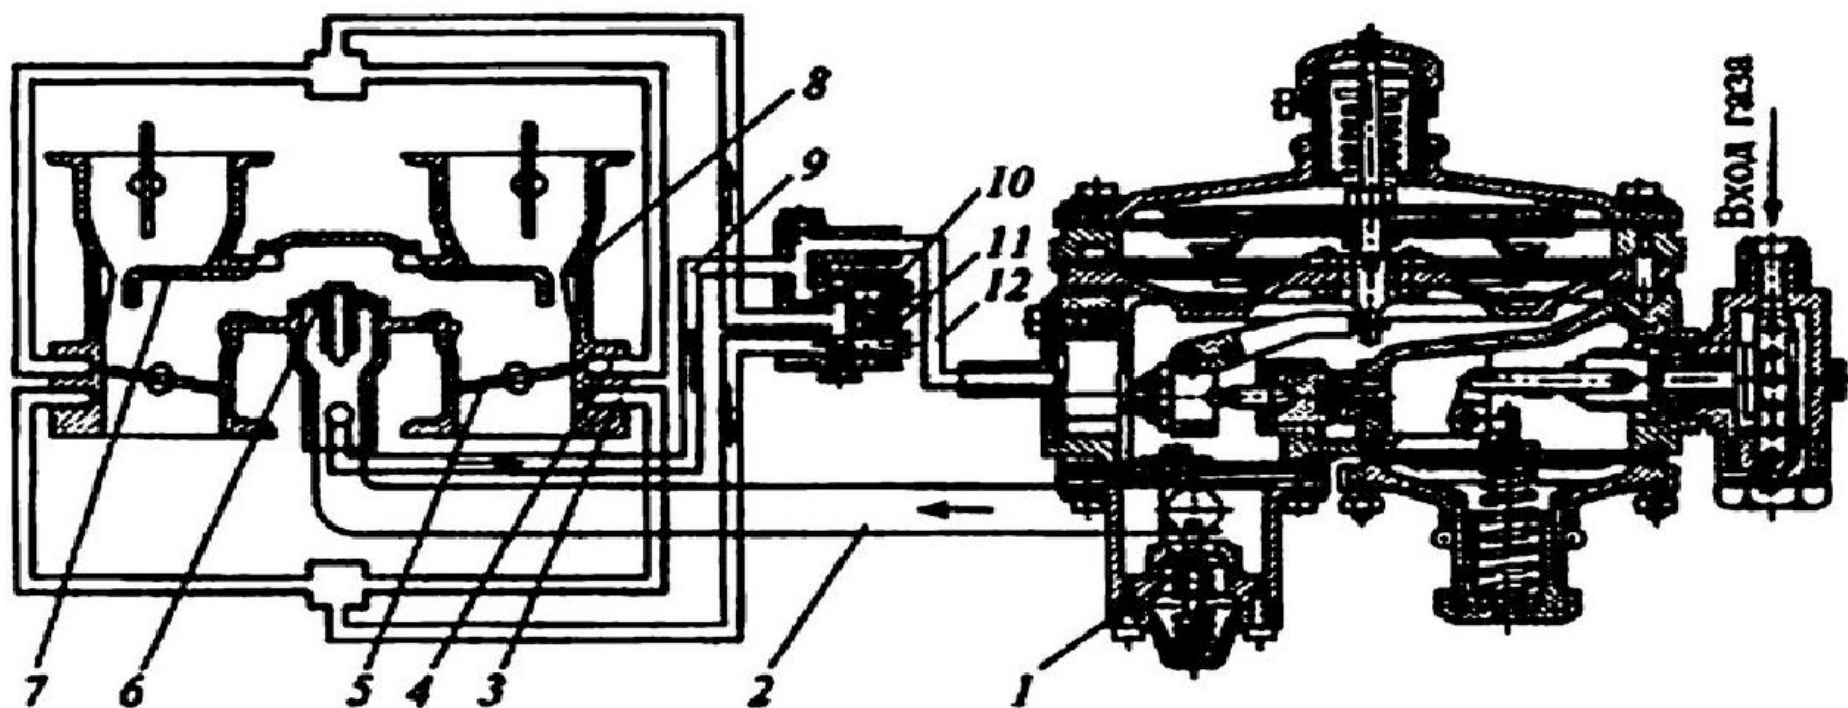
Схема соединения газового смесителя и двухступенчатого редуктора:
